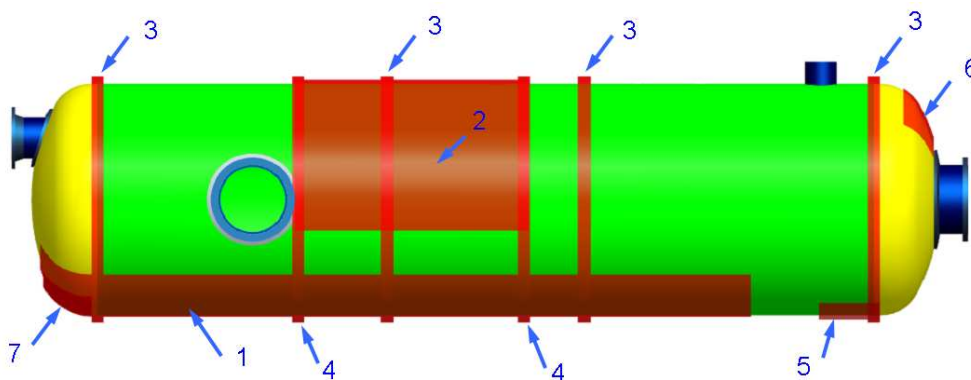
Desenho Esquemático das Regiões de Inspeção.
